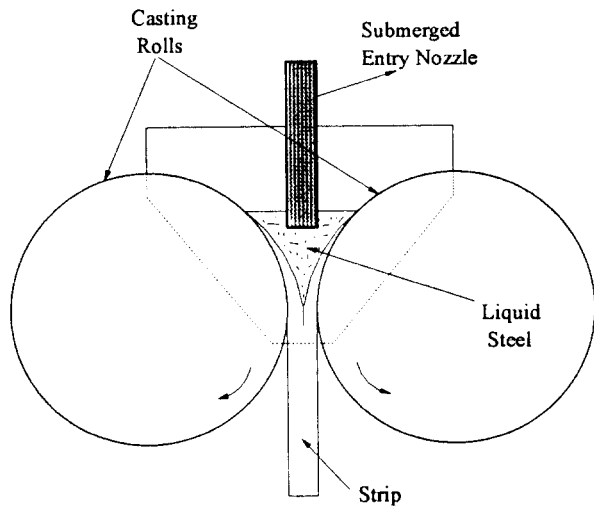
Schematic Sketch of the Twin Roll Strip Casting Process
